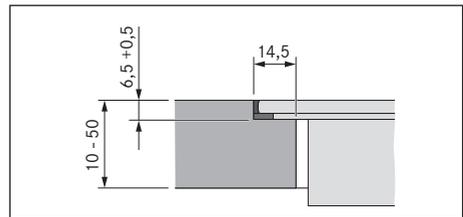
Dimension d'encadrement pour un montage affleurant
